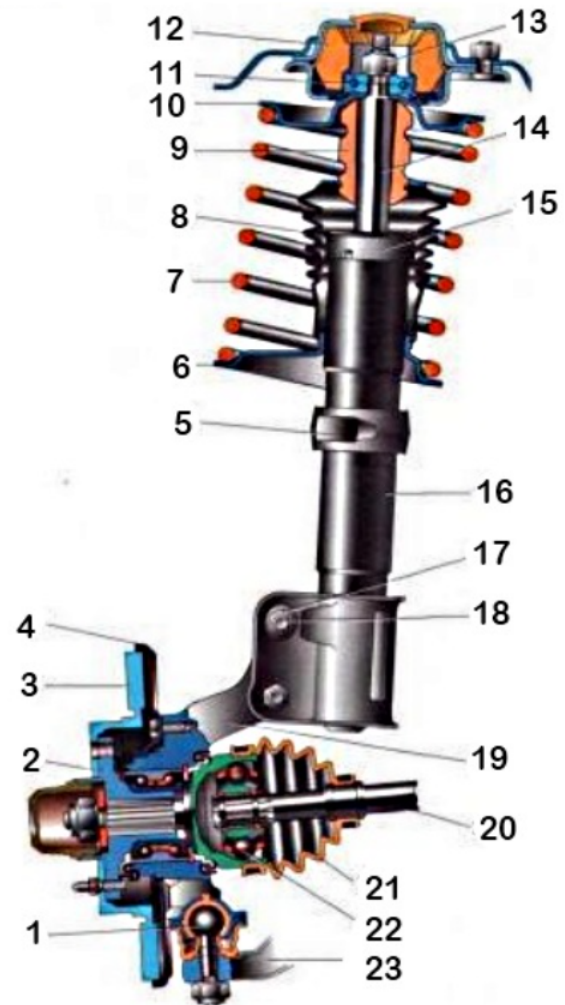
Конструкція підвіски типу МакФерсон.
